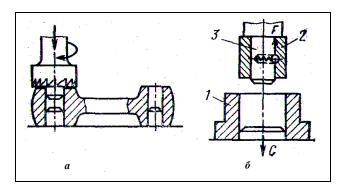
Установка заготовки без закрепления: а – при обработке торца; б – при сборке
